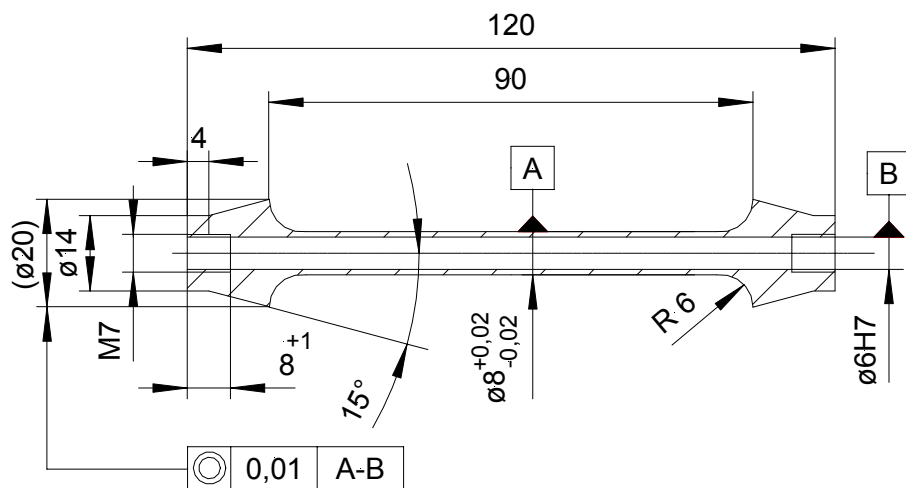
Probengeometrie für Umwandlungen unter Druckspannungen.
